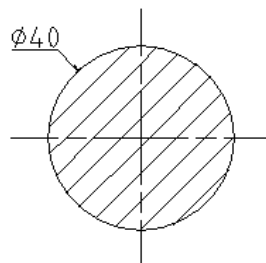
Sección del árbol en la sección de la empaquetadura.
